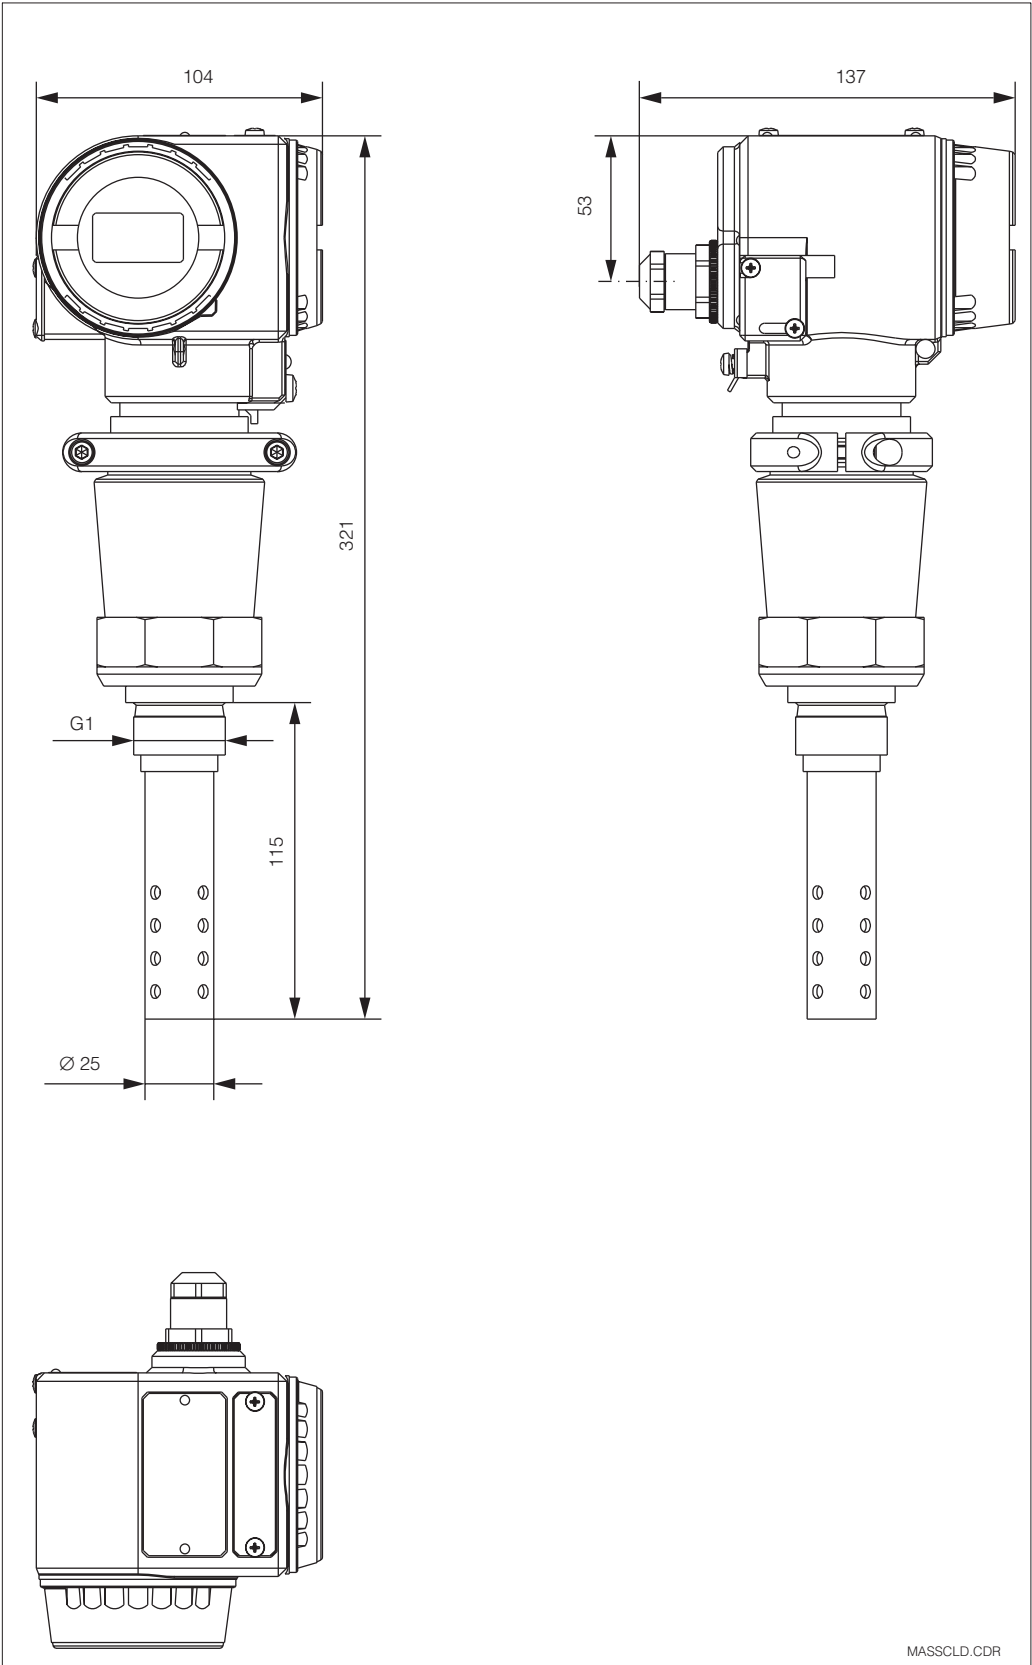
Dimensions Mypro CLD 431 avec CLS 12
